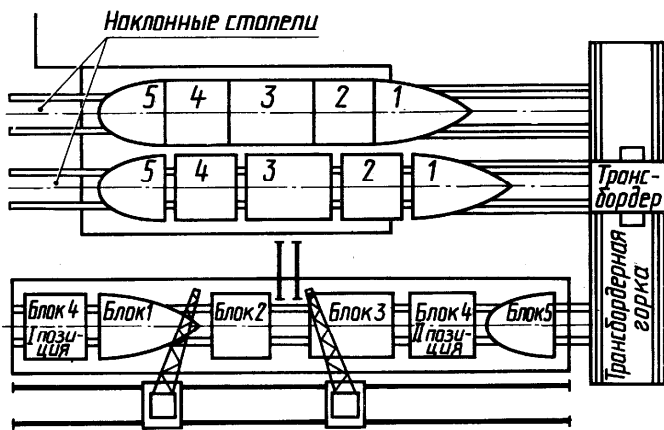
Схема сборки корпуса корабля на стапеле блочным методом
